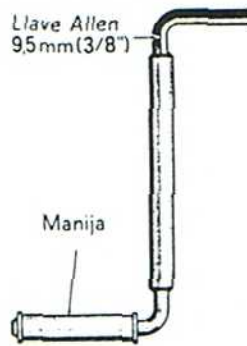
Herramienta para hacer girar el rotor 8268440.
